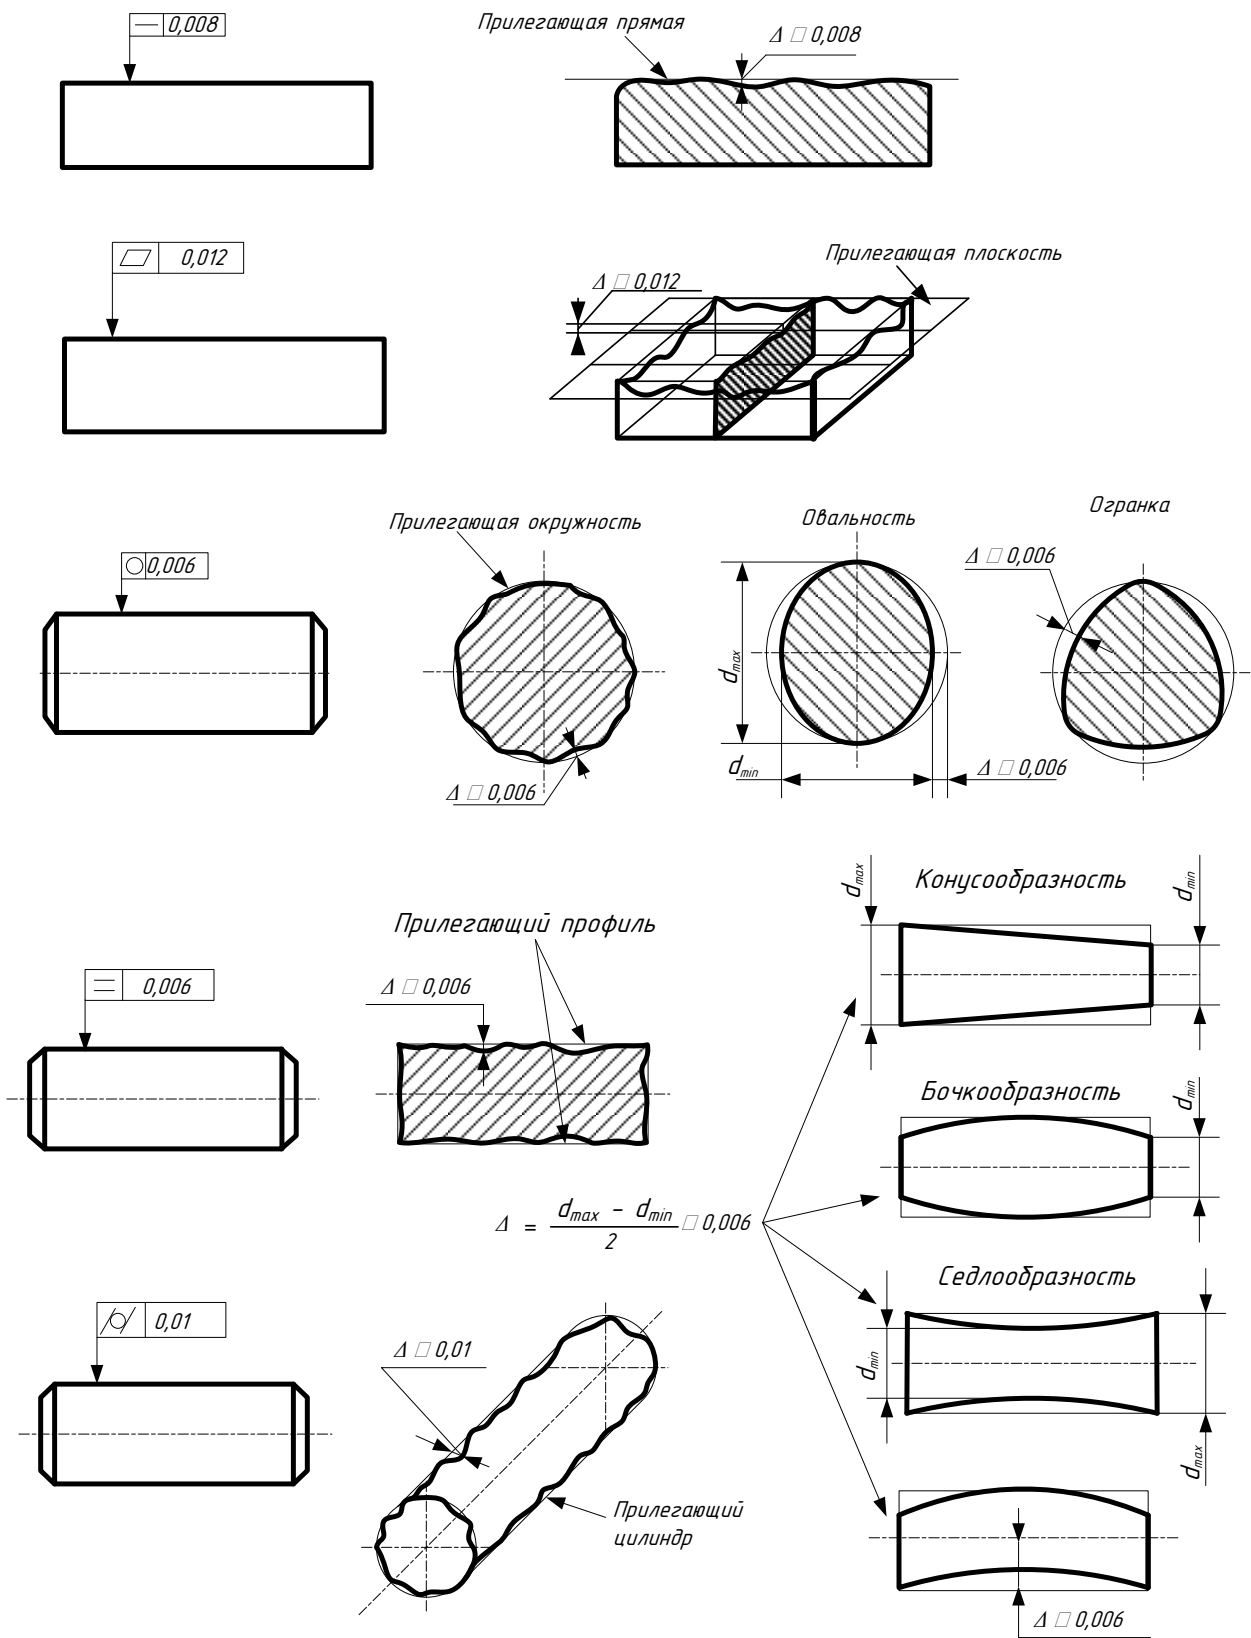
Обозначения и определение параметров допусков формы
